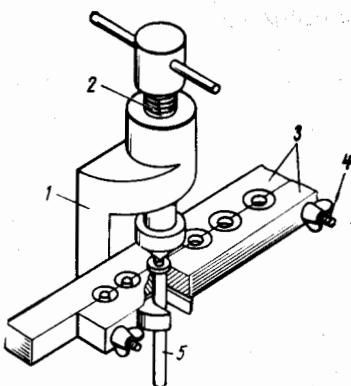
Приспособление для развалцовки концов топливопроводов:
